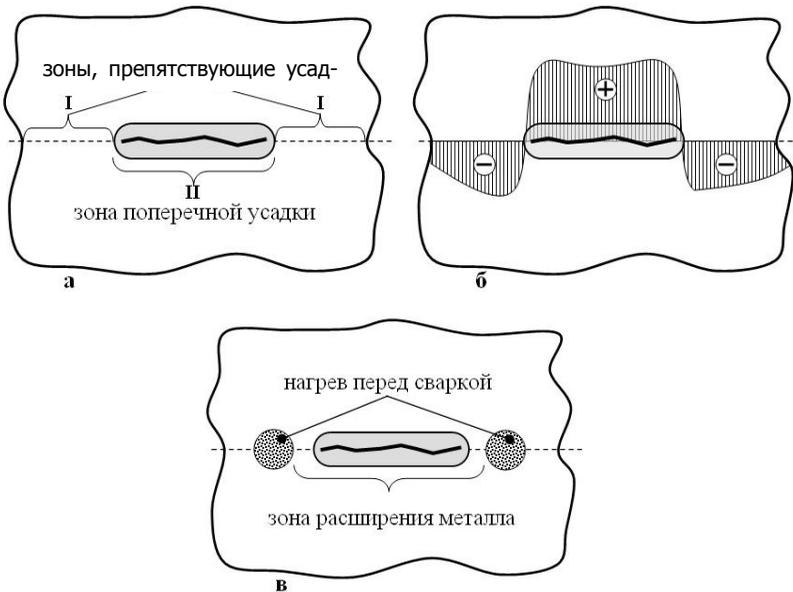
Обеспечение условий для свободного протекания поперечной усадки при ремонте конструкции с трещиной
